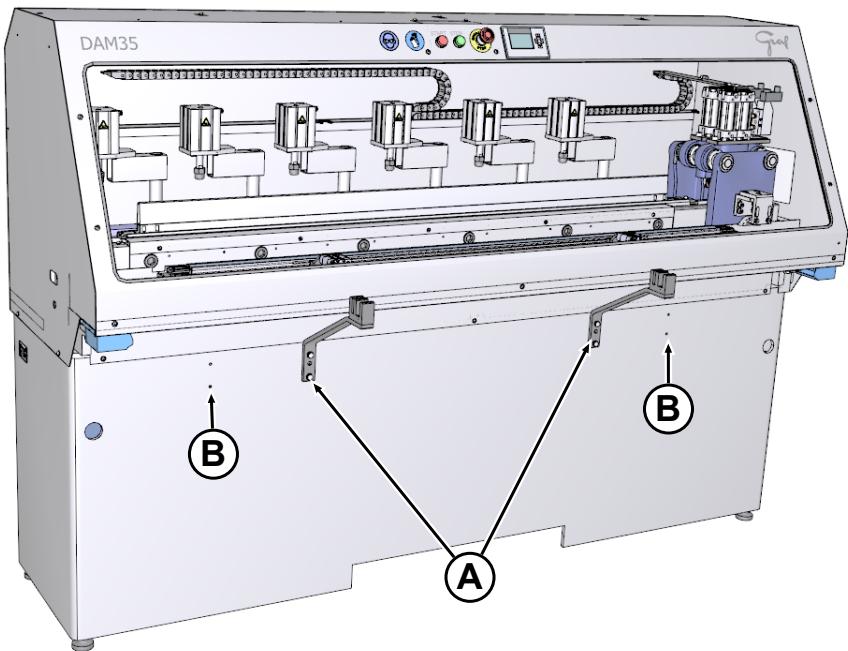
Posições possíveis dos suportes para o chapéu de cardagem
